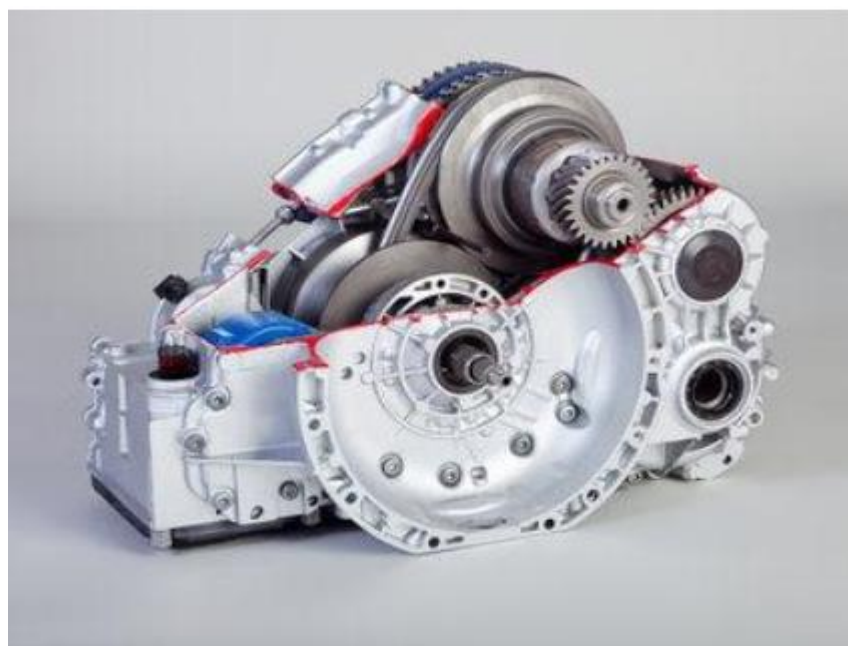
Вариатор *Autotronic 722.8
